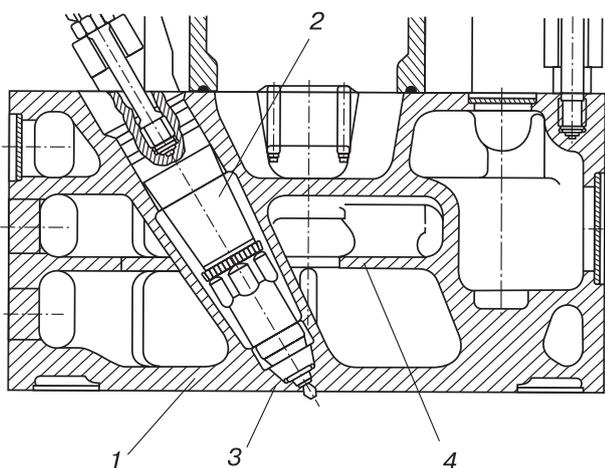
Вид крышки дизеля 5D49 (разрез по форсунке):
